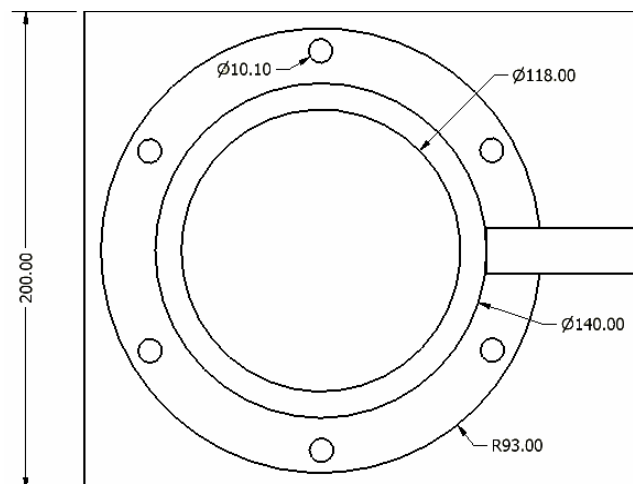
7. Dimensiones de las bridas de las placas soporte a la columna de la prensa. Fuente: Los Autores.
